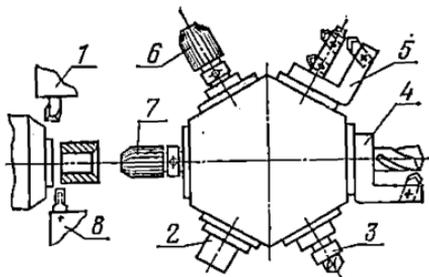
Схема настройки токарно-револьверного станка для изготовления гладкой втулки:
